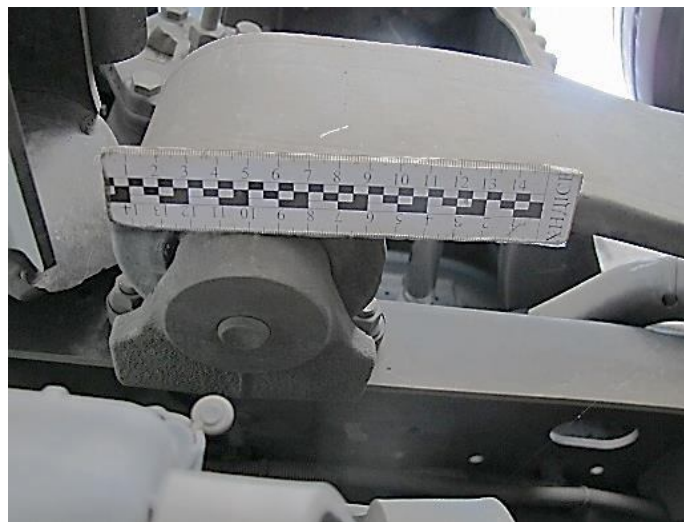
Детальний вигляд кріплення ресори підвіски правого переднього колеса автомобіля MAN TGM
